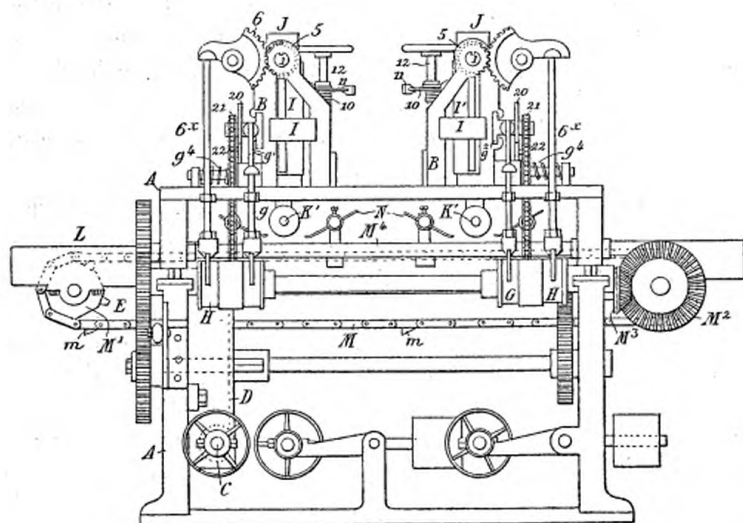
Machine à moulurer Van Houten, vue de côté.
